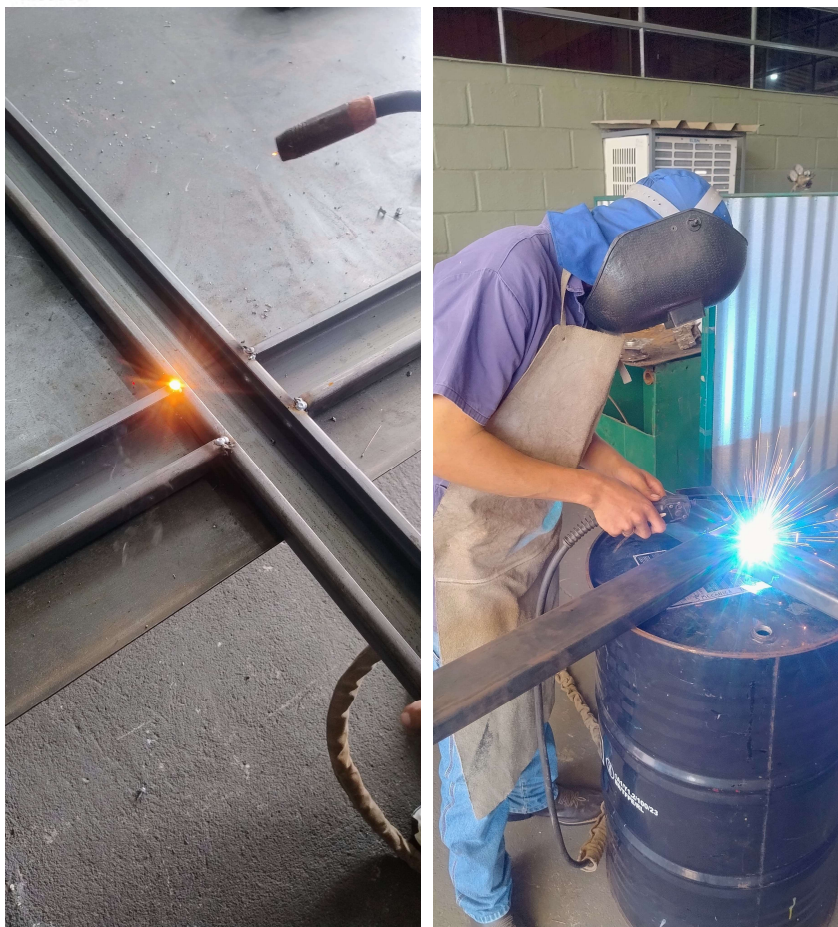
Soldagem da cruzeta (estrutura inferior do touro)
